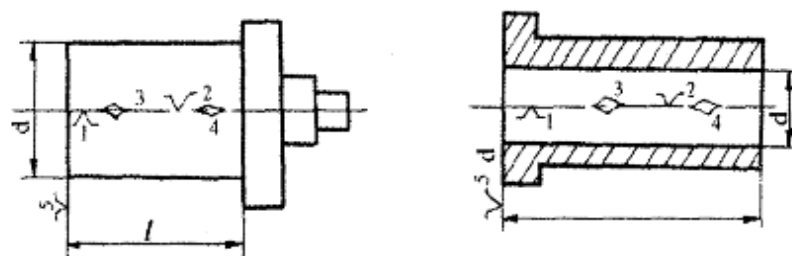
Теоретичні схеми базування заготовок типу тіл обертання з використанням осі, як бази
